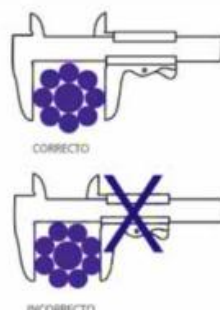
Inspección dimensional del cable de acero.
